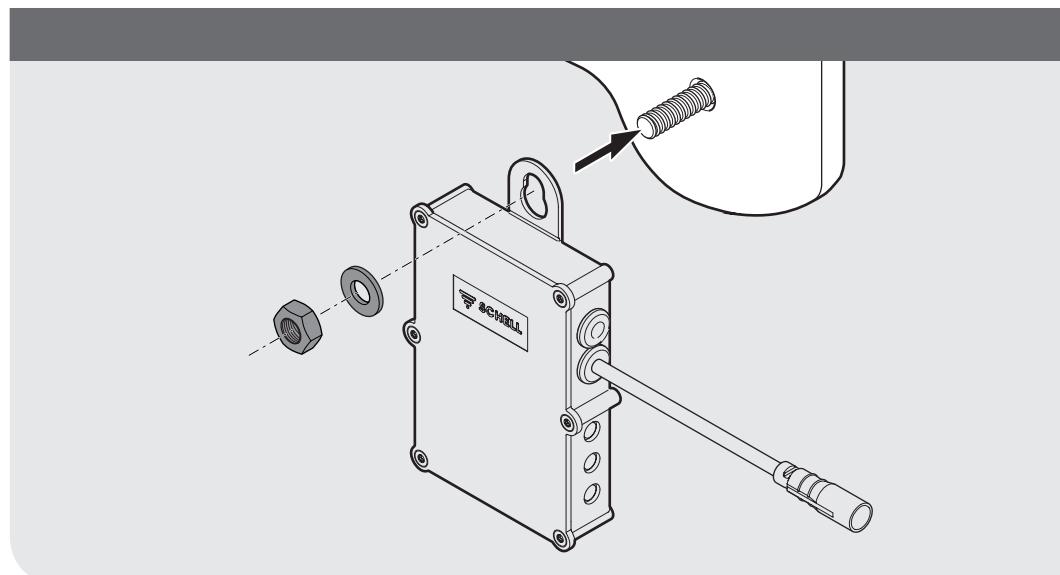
Montage apparent sous le lavabo, exemple d'un extendeur de bus eSCHELL BE-K
